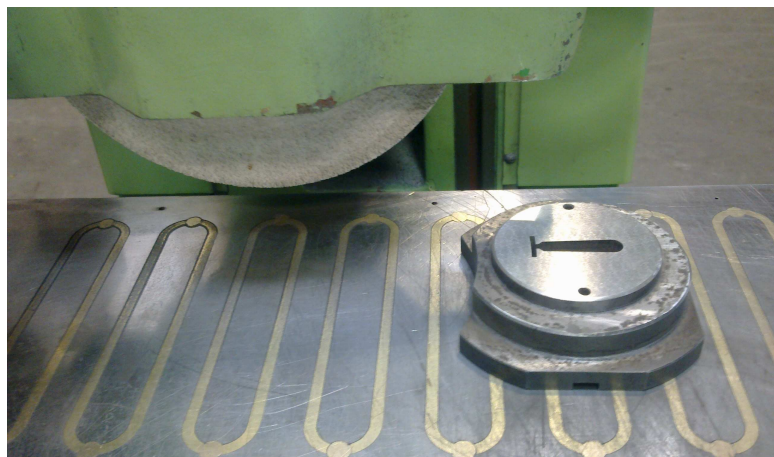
Bruska 3E 756 v lisovně společnosti TES a.s.
